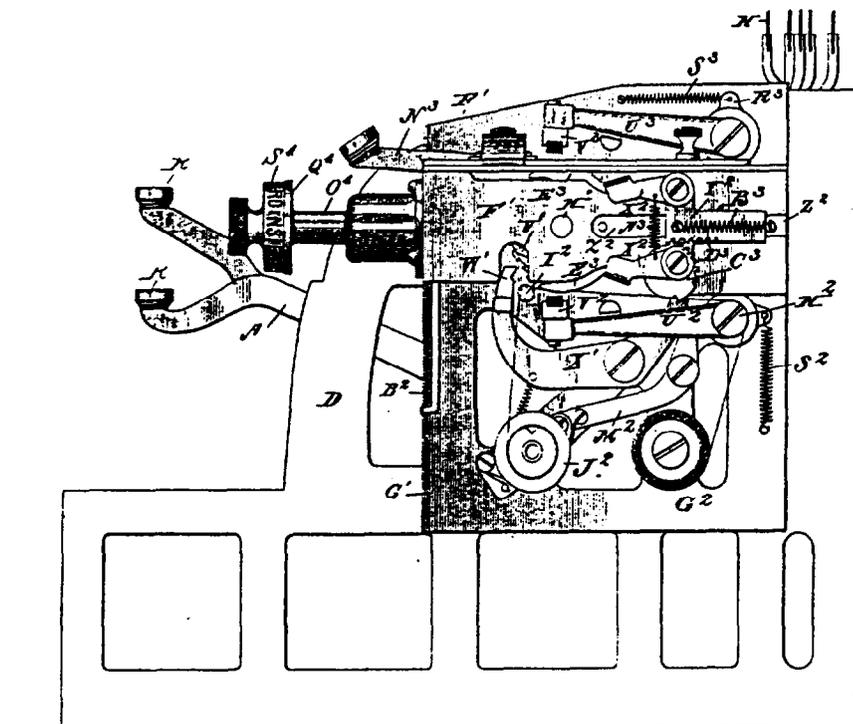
Caissier Carney. Vue par bout de droite (fig. 121 bis).
